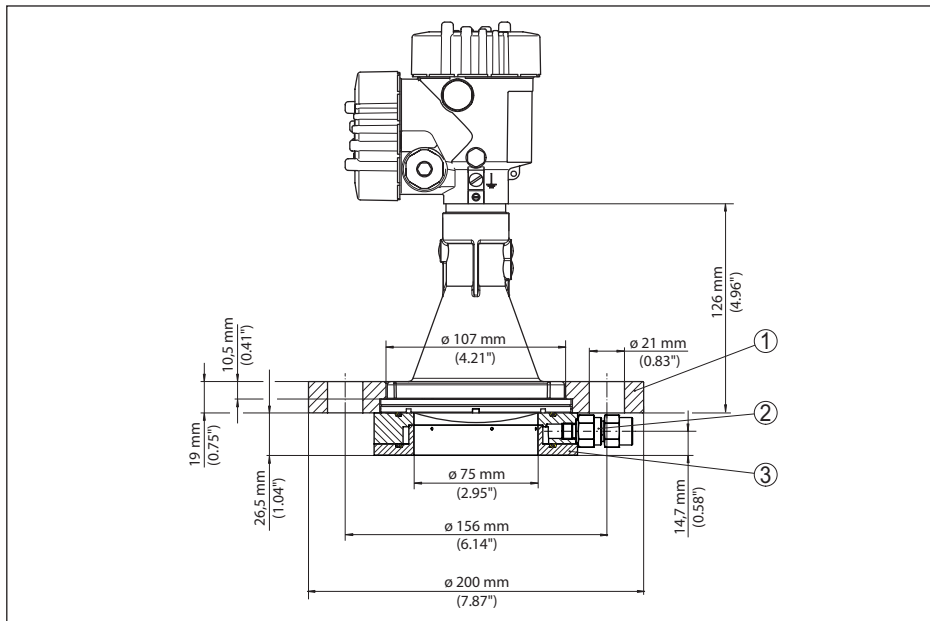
VEGAPULS 6X com flange de capa e conexão de ar de limpeza adequado para 3" 150 lbs, DN 80 PN 16
